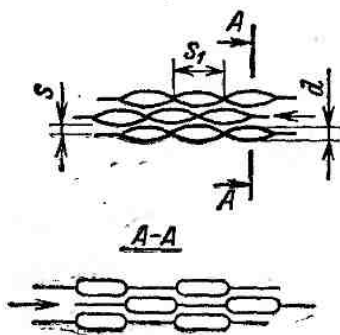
Каналы волнообразные пластинчатых воздухоподогревателей с профильными поверхностями
